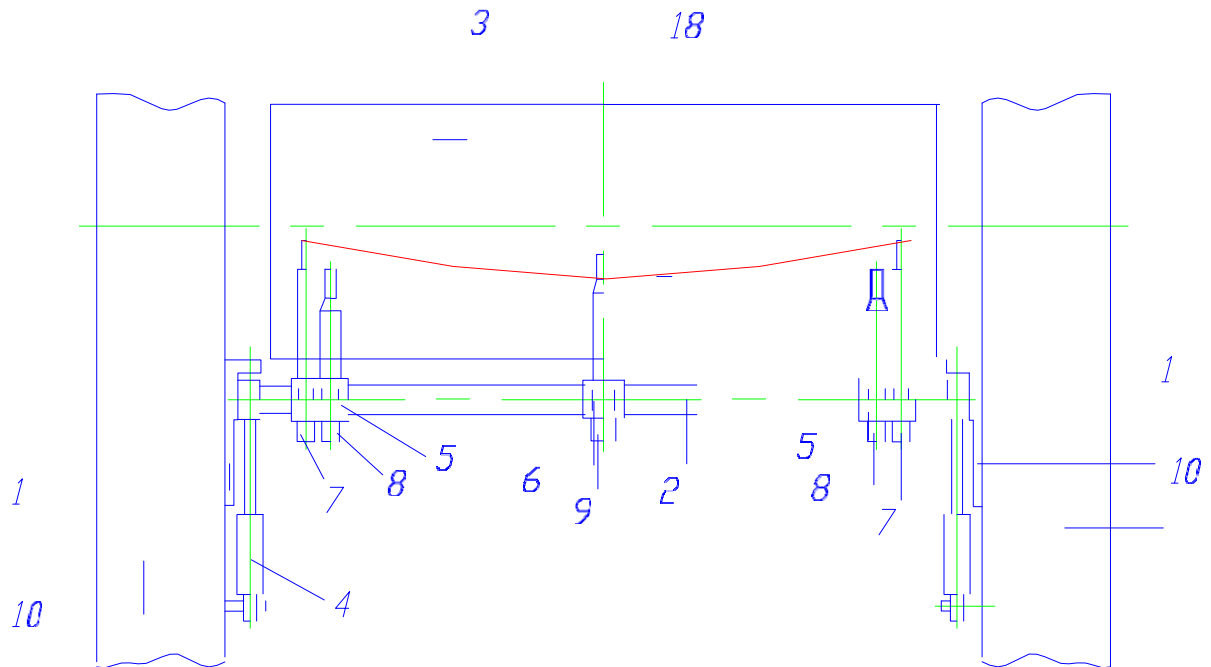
Схема пристрою для регулювання запасу матеріалу перед валками каландру.
